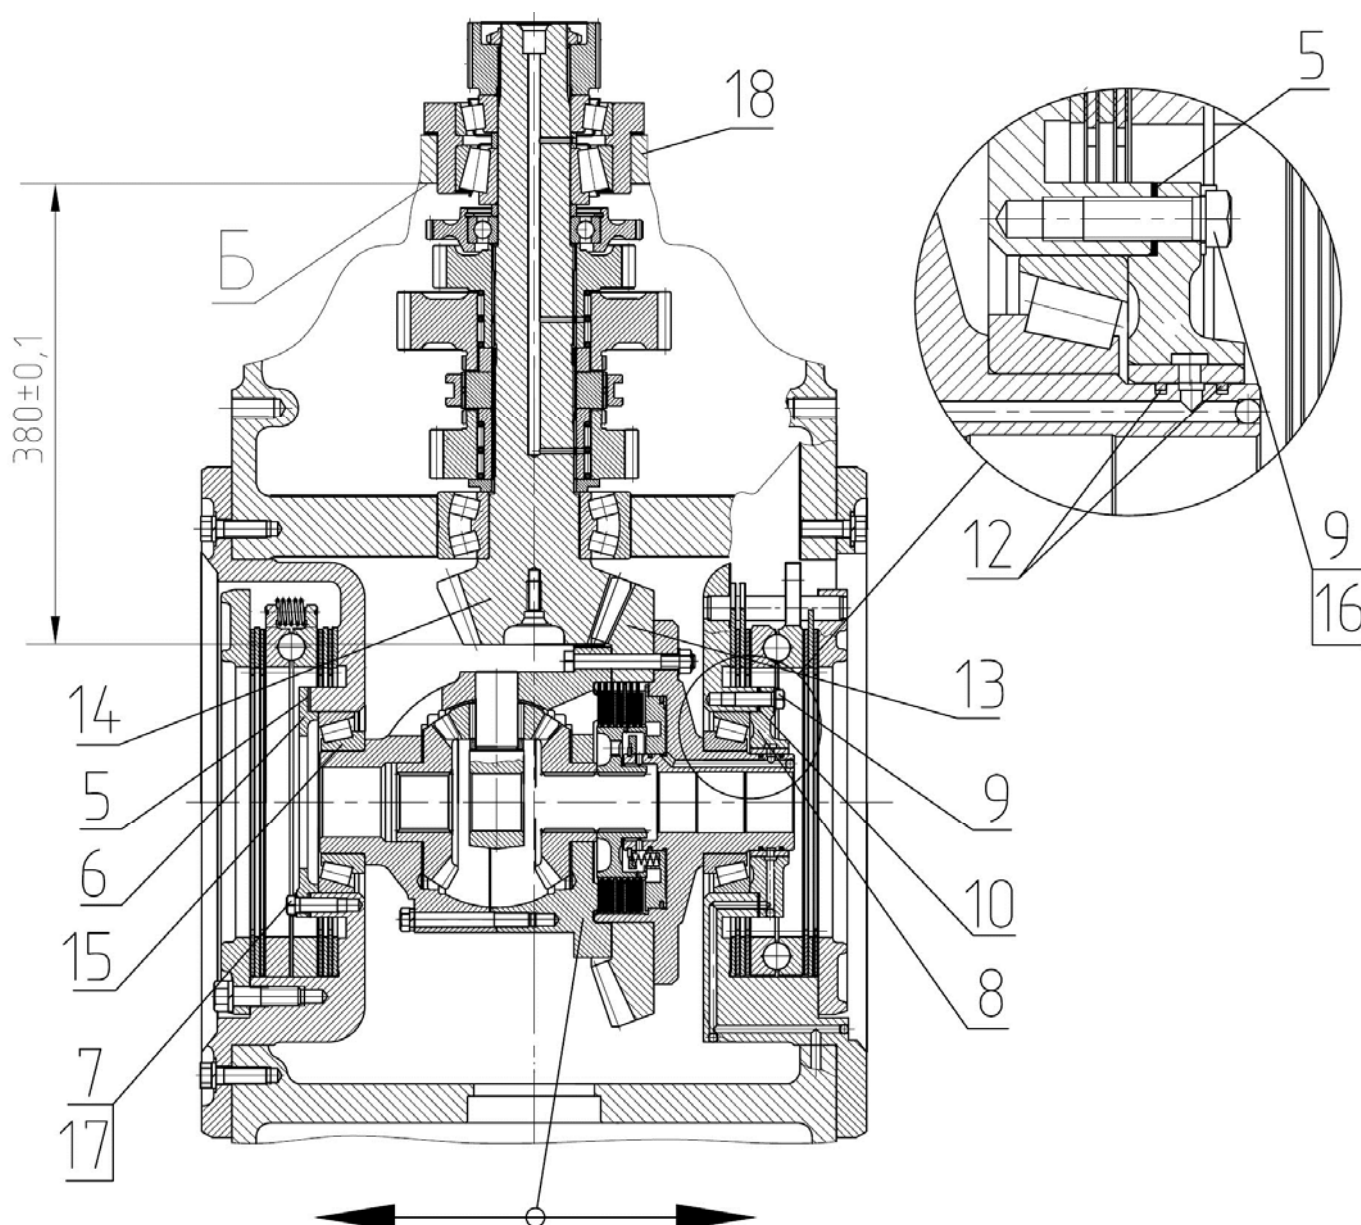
Регулировка бокового зазора в шестернях главной пары.
